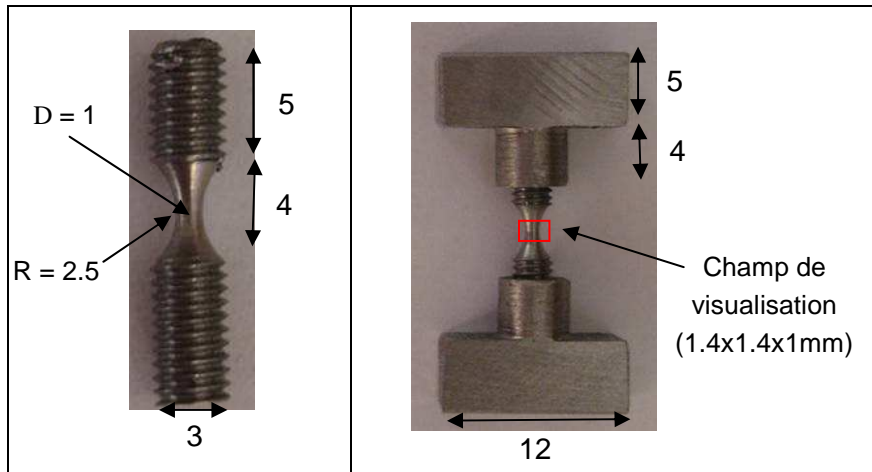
Dimensions (mm) des éprouvettes de tomographie et montage expérimental
